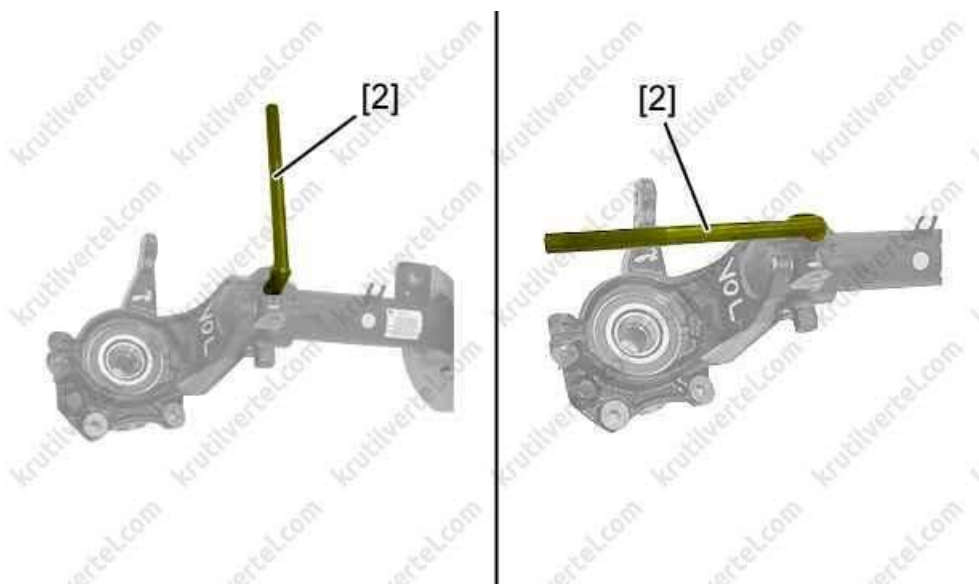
Розтискання хомута поворотного кулака:
